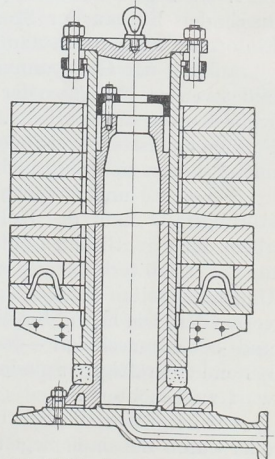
Druckwasserspeicher. Der Zylinder bewegt sich auf einem ruhenden Kolben.
